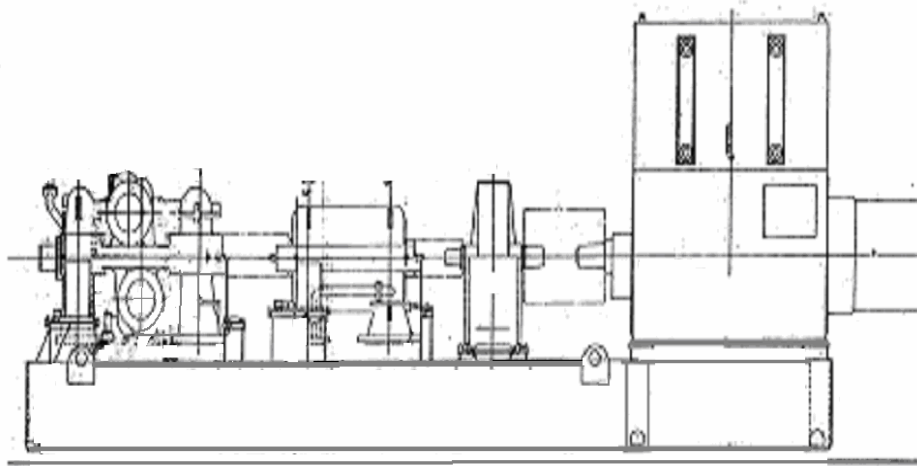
CONJUNTO COMPRESSOR 105-J
